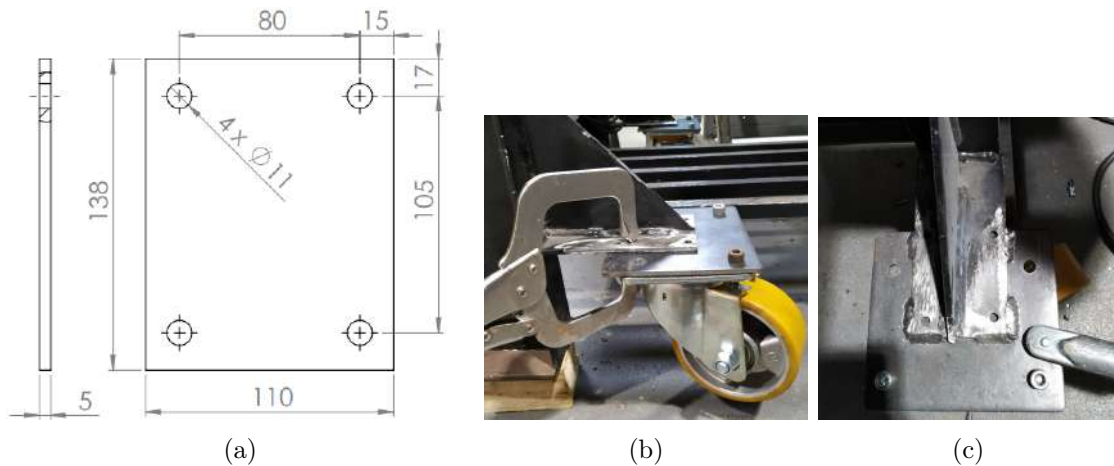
Aplicação dos rodízios na máquina: (a) Desenho de definição da chapa de adaptação, (b) Preparação da chapa para soldadura, (c) Fotografia da soldadura e aplicação dos rodízios na máquina.
